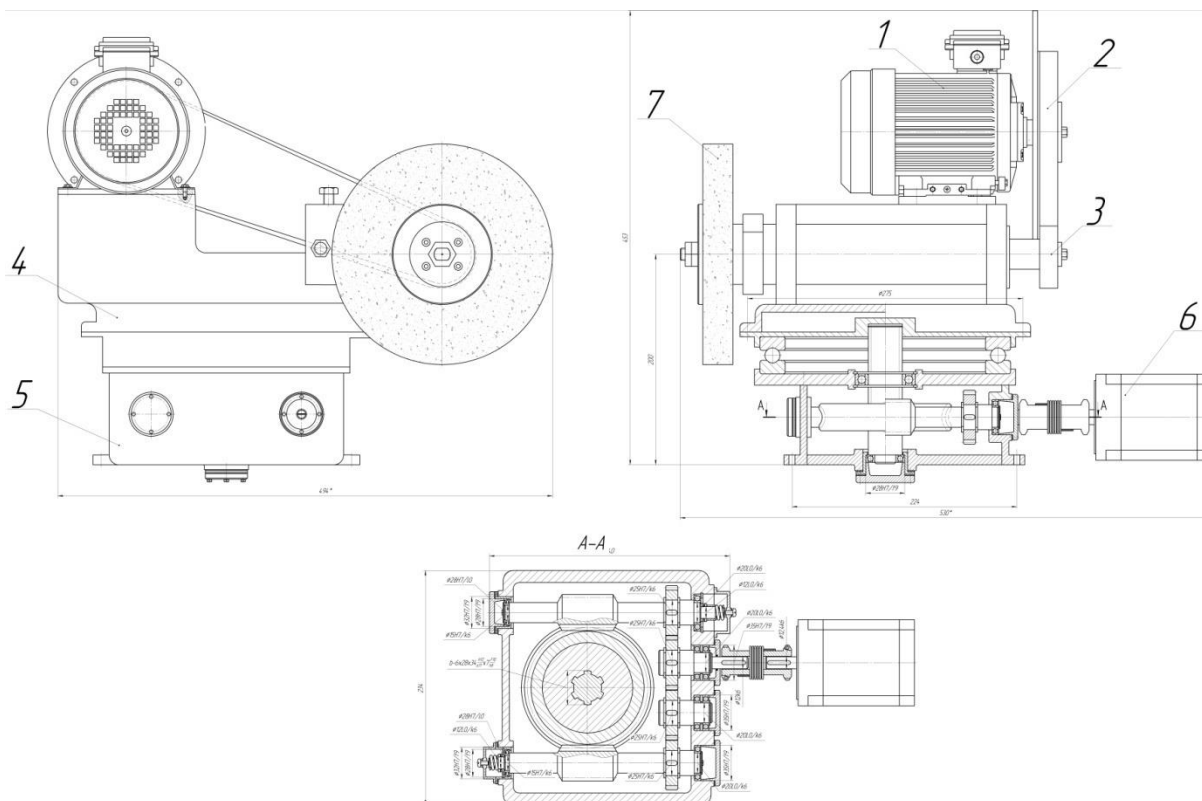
Конструкция модернизированной шлифовальной бабки и поворотного устройства (1 – двигатель привода круга, 2 – ременная передача, 3 – шпиндельный узел, 4 – корпус, 5 – поворотное устройство, 6 – шаговый двигатель привода поворотного устройства, 7 – шлифовальный круг)
